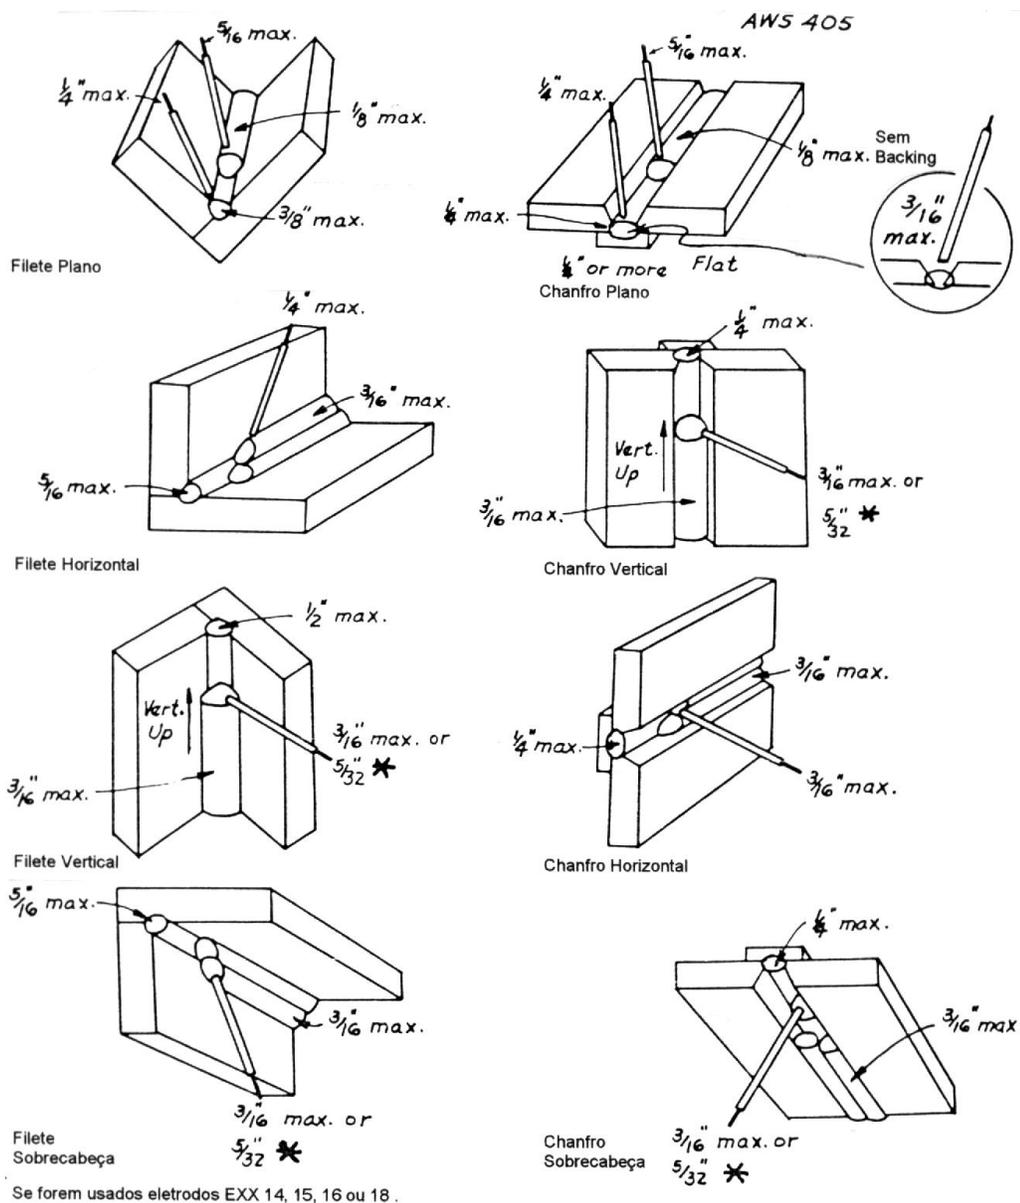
Posições de soldagem e diâmetro dos eletrodos.
